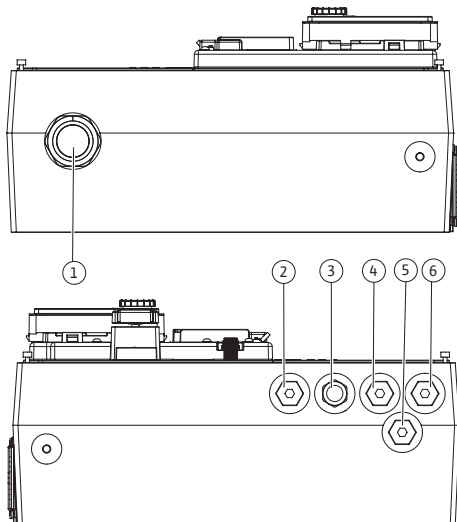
Kabelverschraubungen/Kabeldurchführungen (11 kW ... 22 kW)
